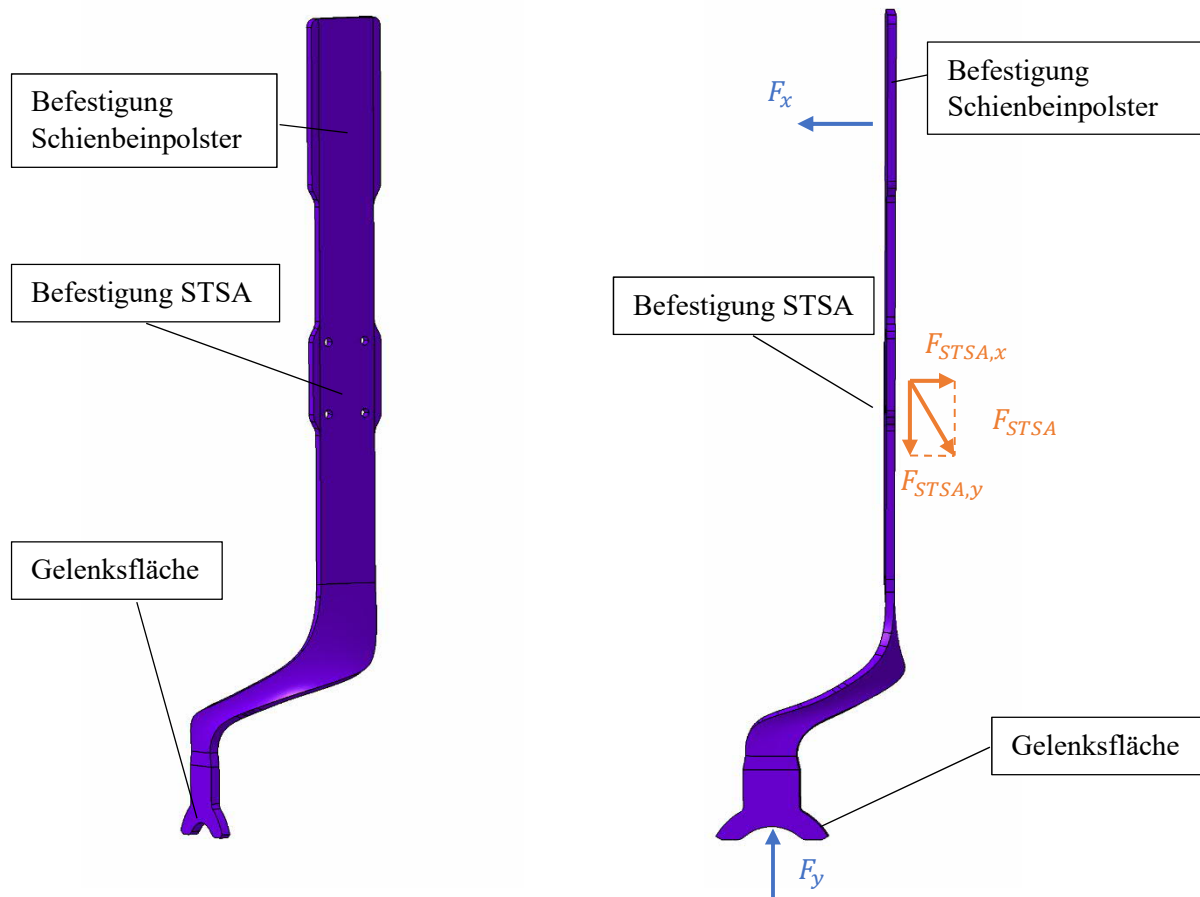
isometrische Ansicht der Schienbeinstütze; zu sehen sind am unteren Ende die konkave Gelenksfläche, auf mittlerer Höhe das Lochbild zur Fixierung des STSAs und oben die Befestigungsposition für die Schienbeinpolsterung
